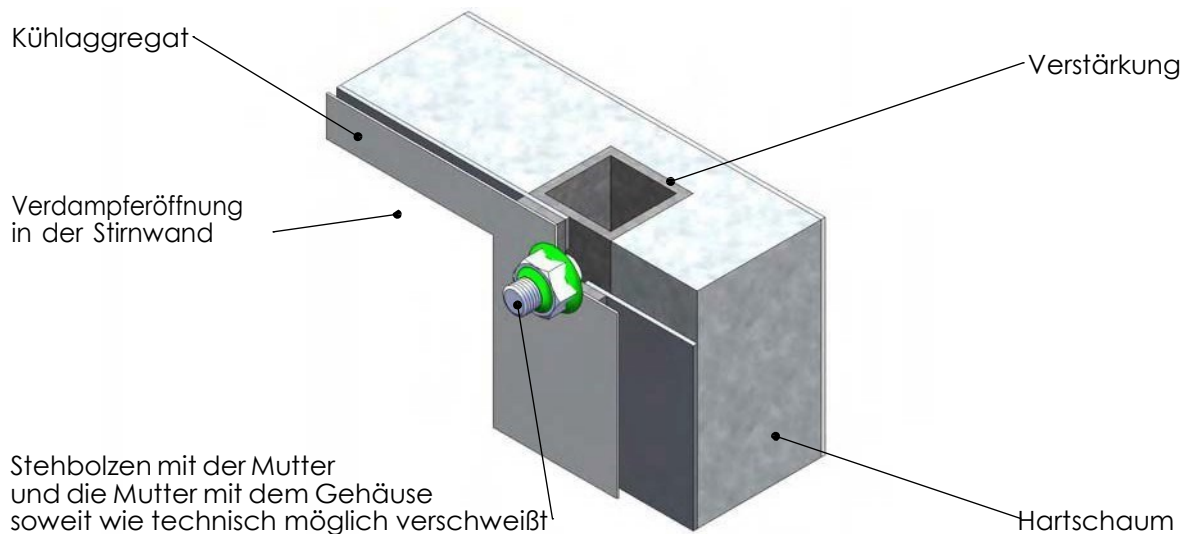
Sicherung mit von innen angebrachten Schrauben
